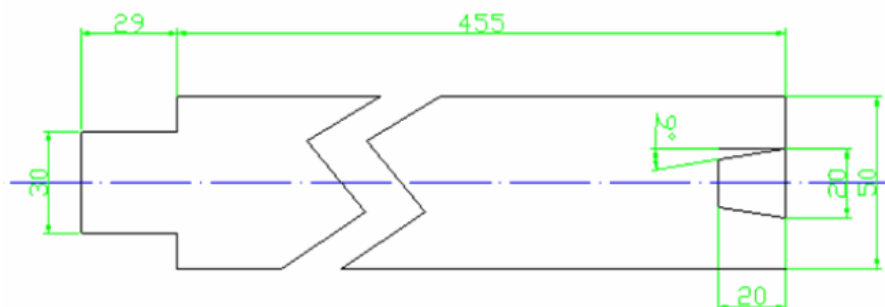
Corpo de prova para os ensaios de temperatura de usinagem
